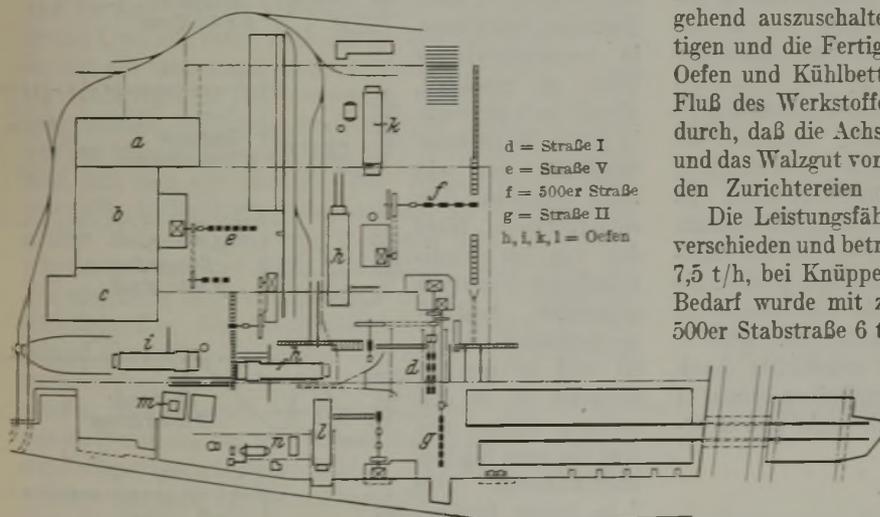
Grundriß der Stabstahl-Walzwerksanlage vor dem Umbau.
